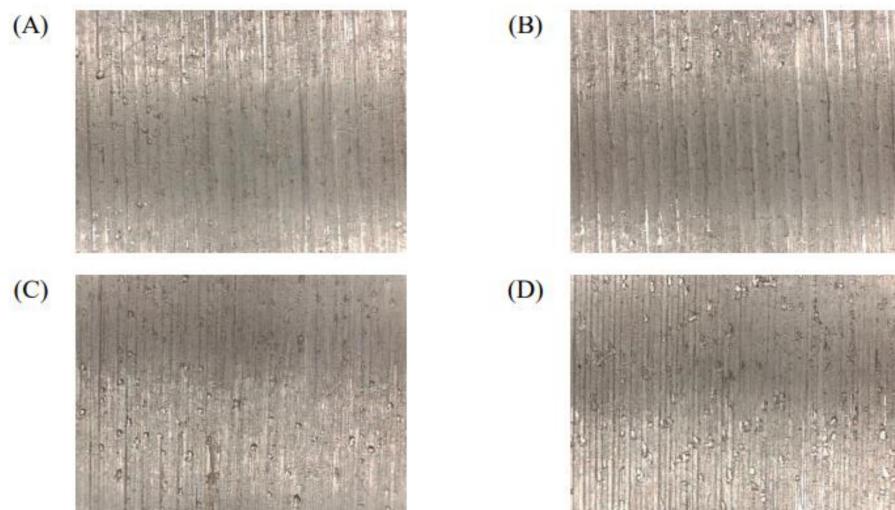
Imagens tiradas da peça usinada com  $V_c = 80\text{ m/min}$  e diferentes avanços (A) Superfície usinada com avanço  $f = 0,10$ , (B) Superfície usinada com avanço  $f = 0,15$ , (C) Superfície usinada com avanço  $f = 0,20$  e (D) Superfície usinada com avanço  $f = 0,25$
